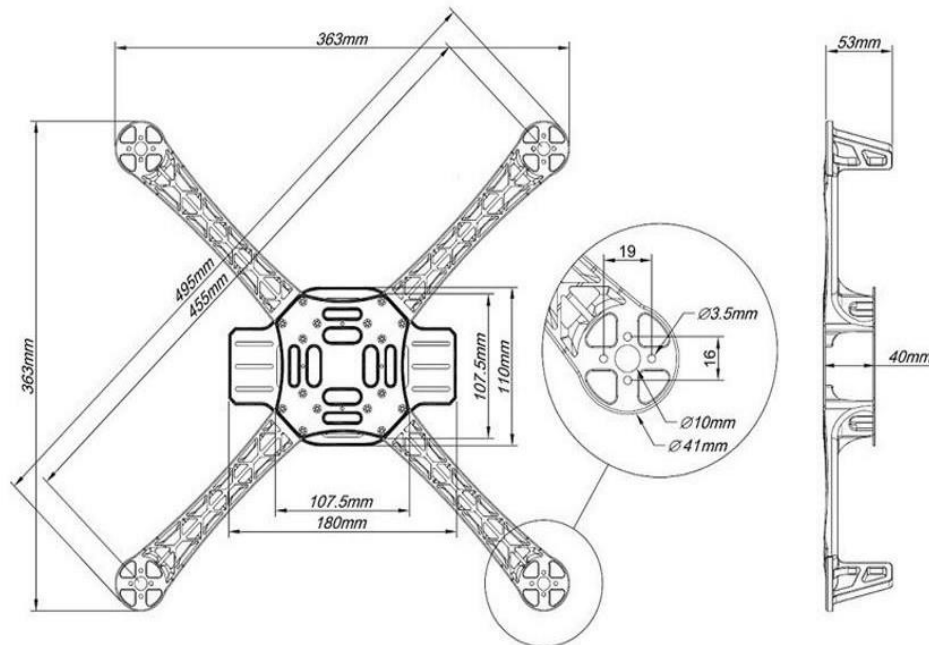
Розміри рами F450 для квадрокоптера на кресленні
